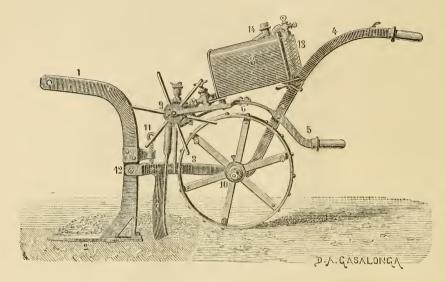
Charrue sulfureuse de M. E. Vernette, de Béziers.
